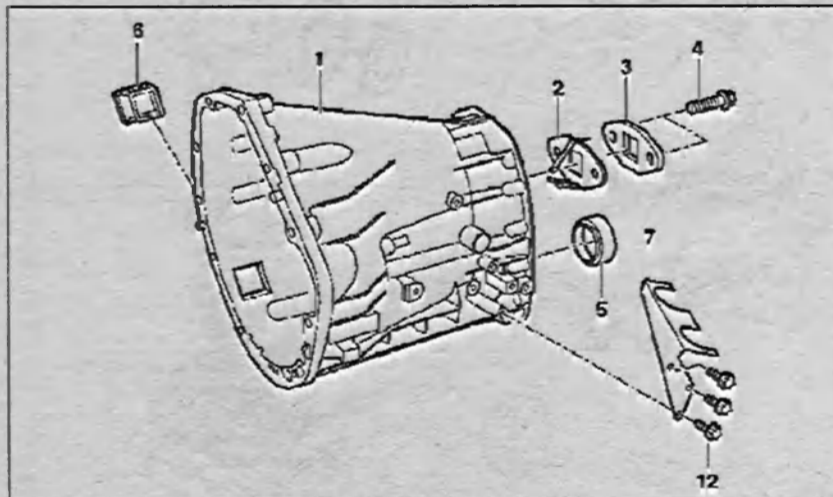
а. Разборка и сборка передней части корпуса МКПП 711.605:
